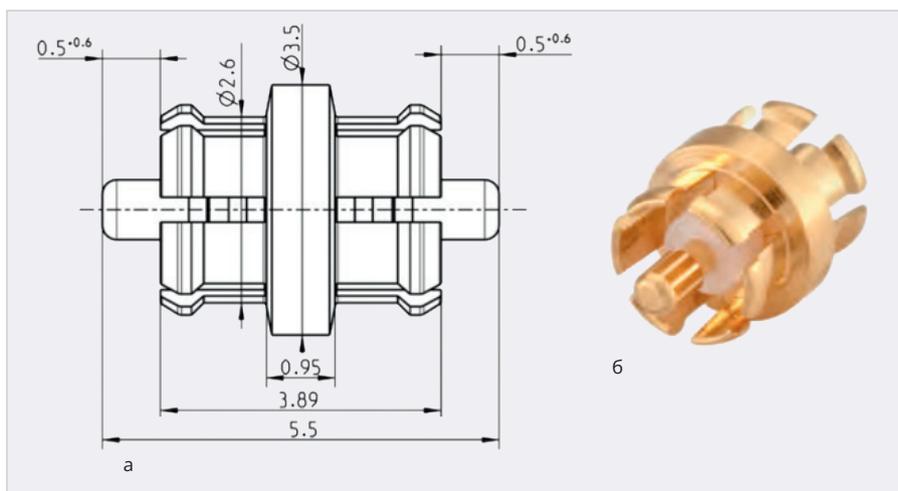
Конструкция (а) и внешний вид (б) адаптера «bullet» FMC
